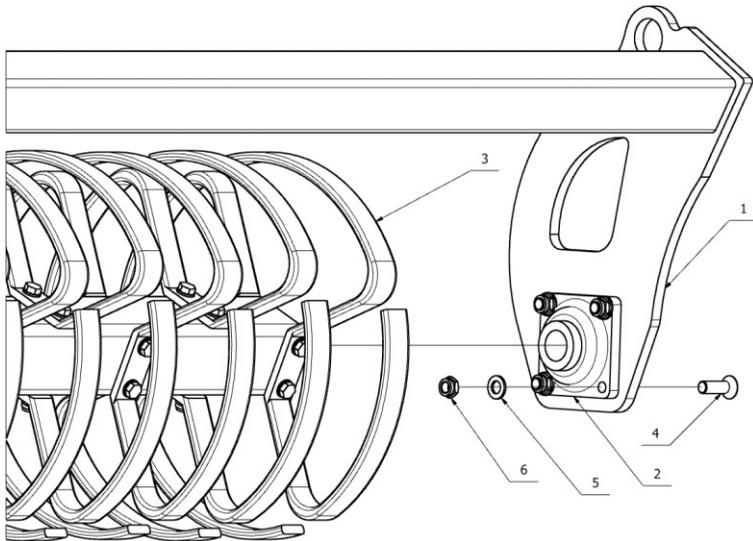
Ø500mm Ringwalze - Lagermontage.
